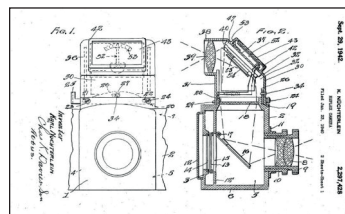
Схематическое устройство фотоаппарата «Спорт»
